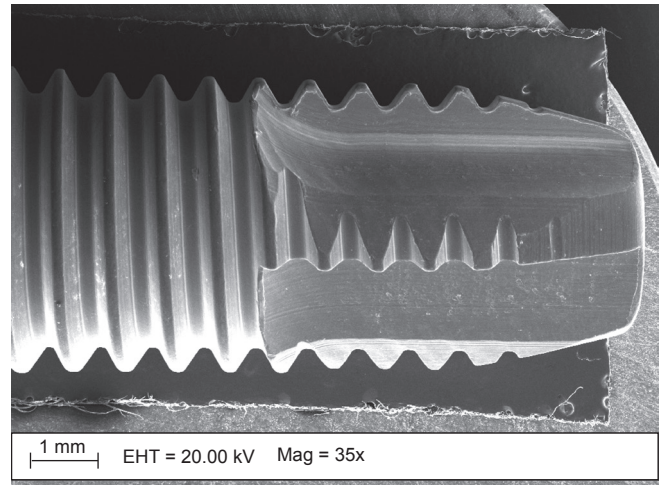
Implantes cilíndricos com superfície usinada antes da inserção.
